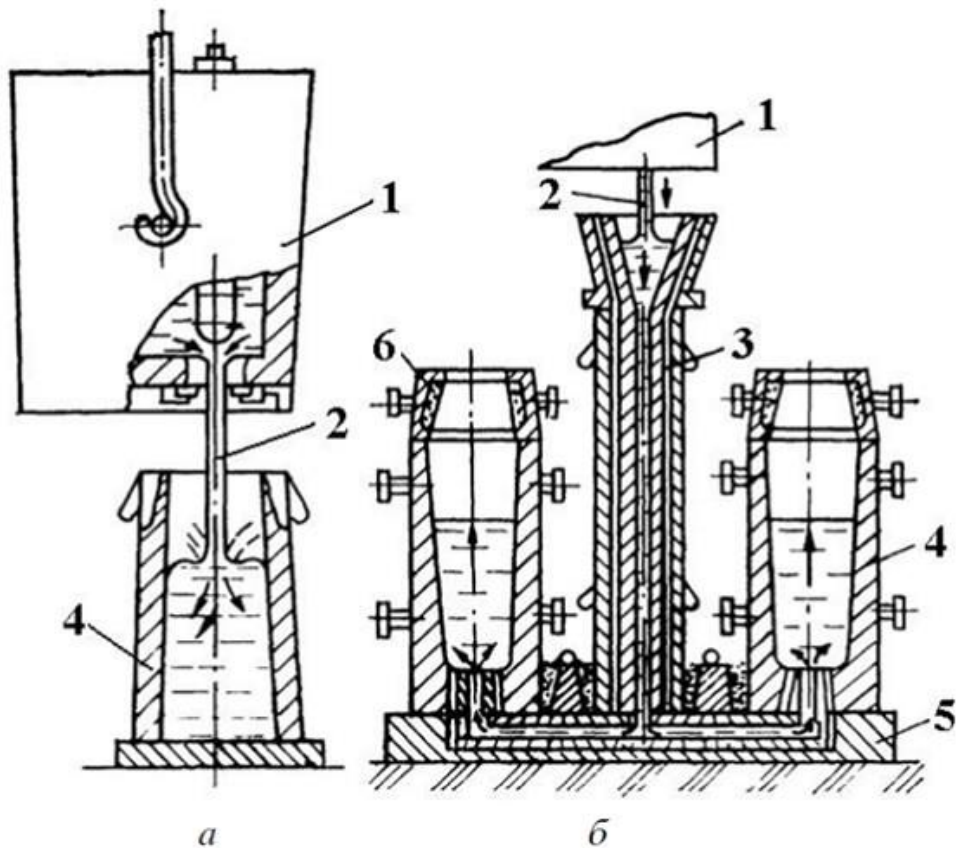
Розливання сталі у виливниці: а – зверху; б – сифоном: 1 – ківш; 2 – метал; 3 – центральний ливник; 4 – виливниці; 5 – піддон; 6 – надставка для утеплення прибутку
